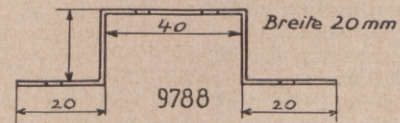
Bügel aus 1 mm-Aluminiumblech zur Befestigung des Filters.
